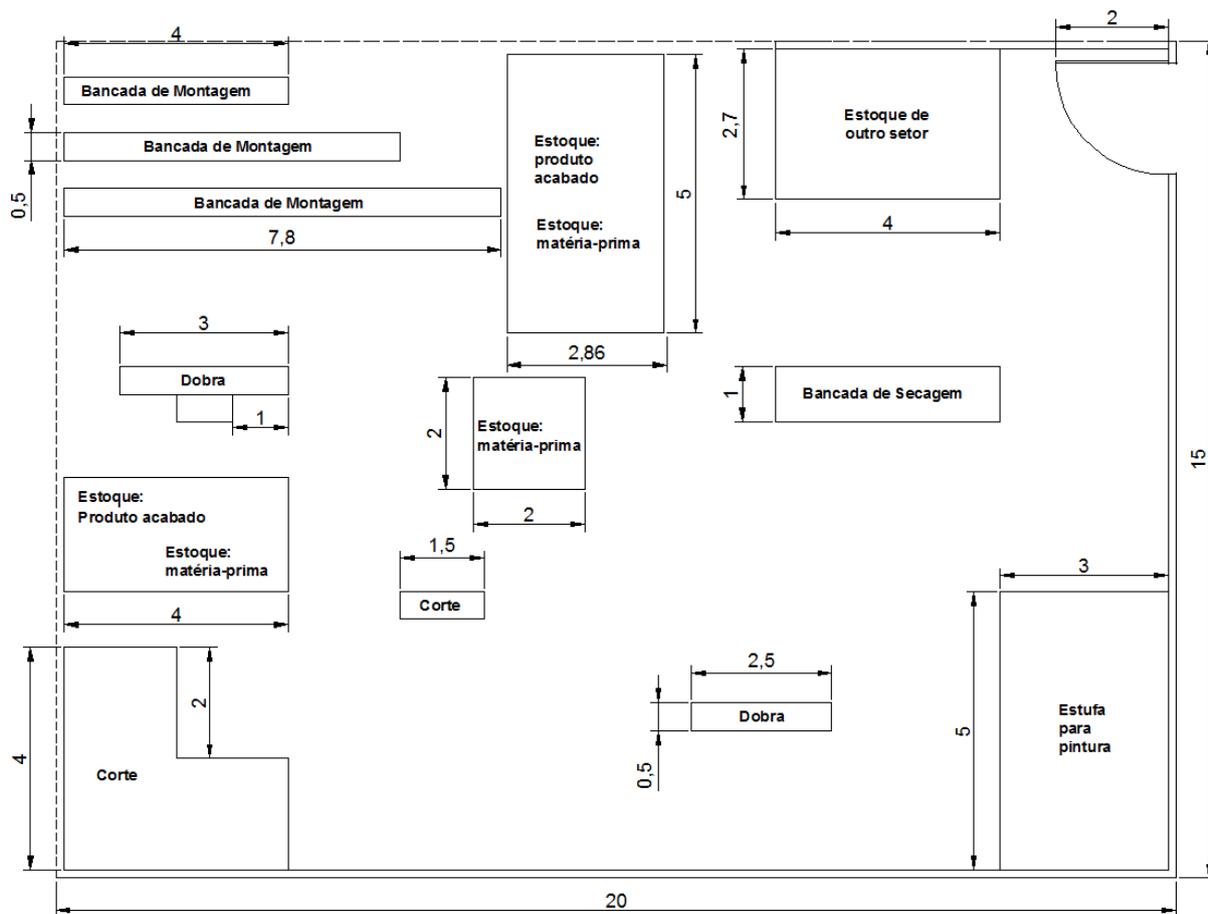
Layout* do setor de calhas e treliça Indústria de pré-fabricados e artefatos de concretos em estudo
